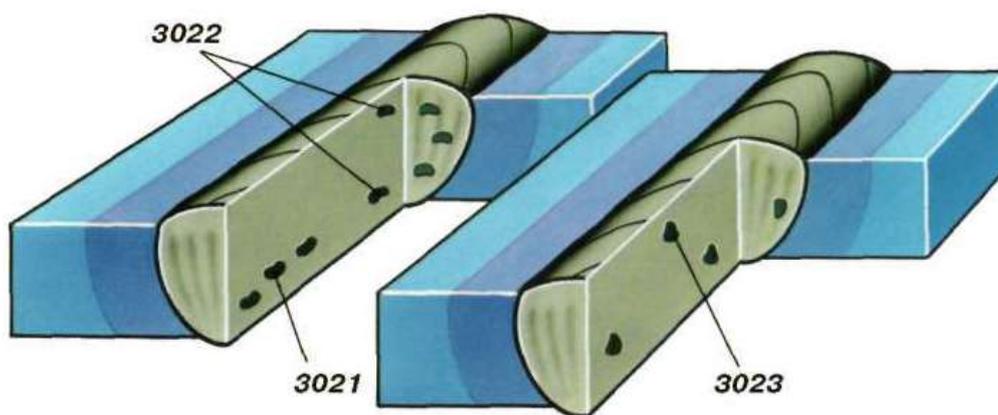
Дефект сварного шва по типу наличия флюсовых включений
